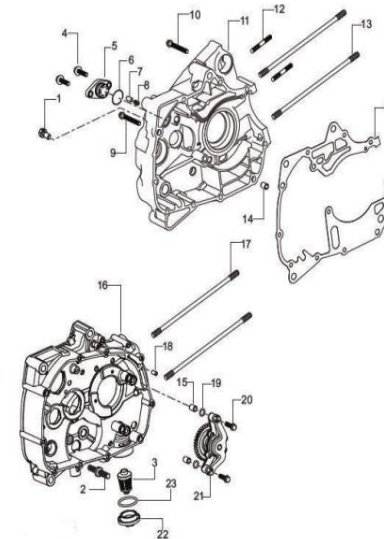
CARCASA DERECHA E IZQUIERDA
